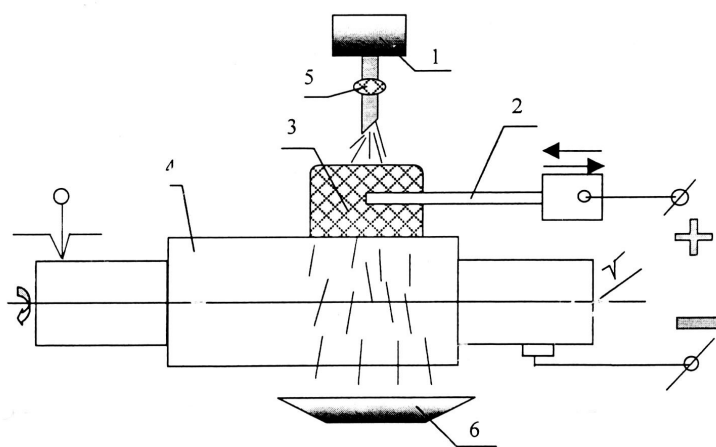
Схема установки для нанесения покрытий электролитическим натиранием на базе токарного станка.
